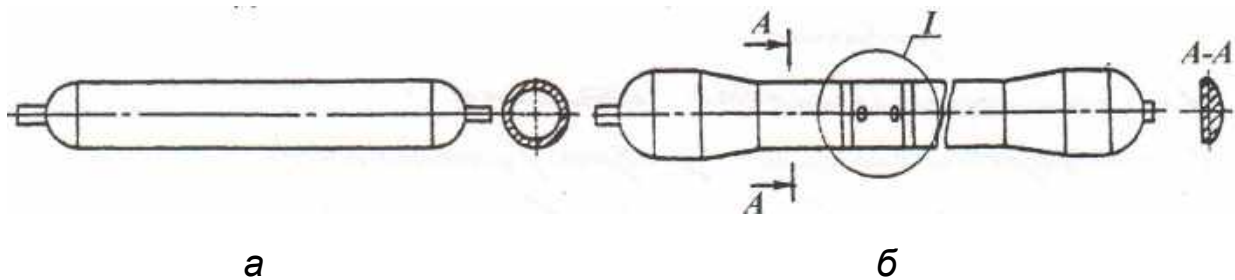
Схеми оправок для намотування деталей: а – нерозбірна металева з конусністю зовнішньої поверхні; б – розбірна металева (l – технологічний припуск)
